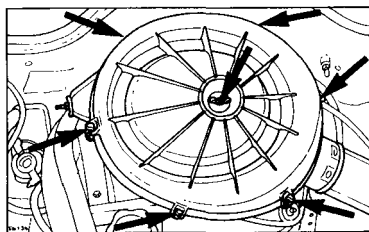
Двигатель OHV — крепежная гайка и зажимы крышки воздушного фильтра (указаны стрелками)
